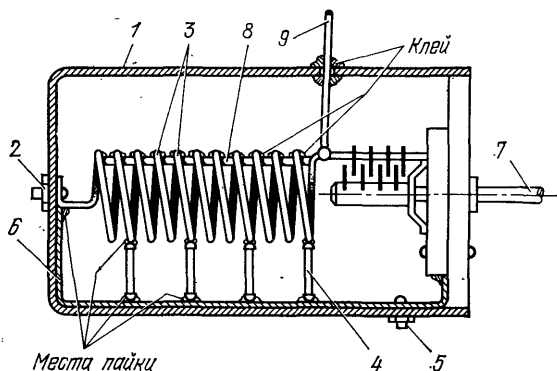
Конструкция КВ контура высокой добротности: 1 — корпус-экран; 2 — узел крепления; 3 — витки катушки; 4 — стойки крепления витков (фарфор); 5 — узел крепления; 6 — полоса из жести; 7 — ось КПЕ; 8 — палочка из фарфора или ВЧ феррита, приклеенная полистироловым клеем; 9 — вывод (вклеен)
